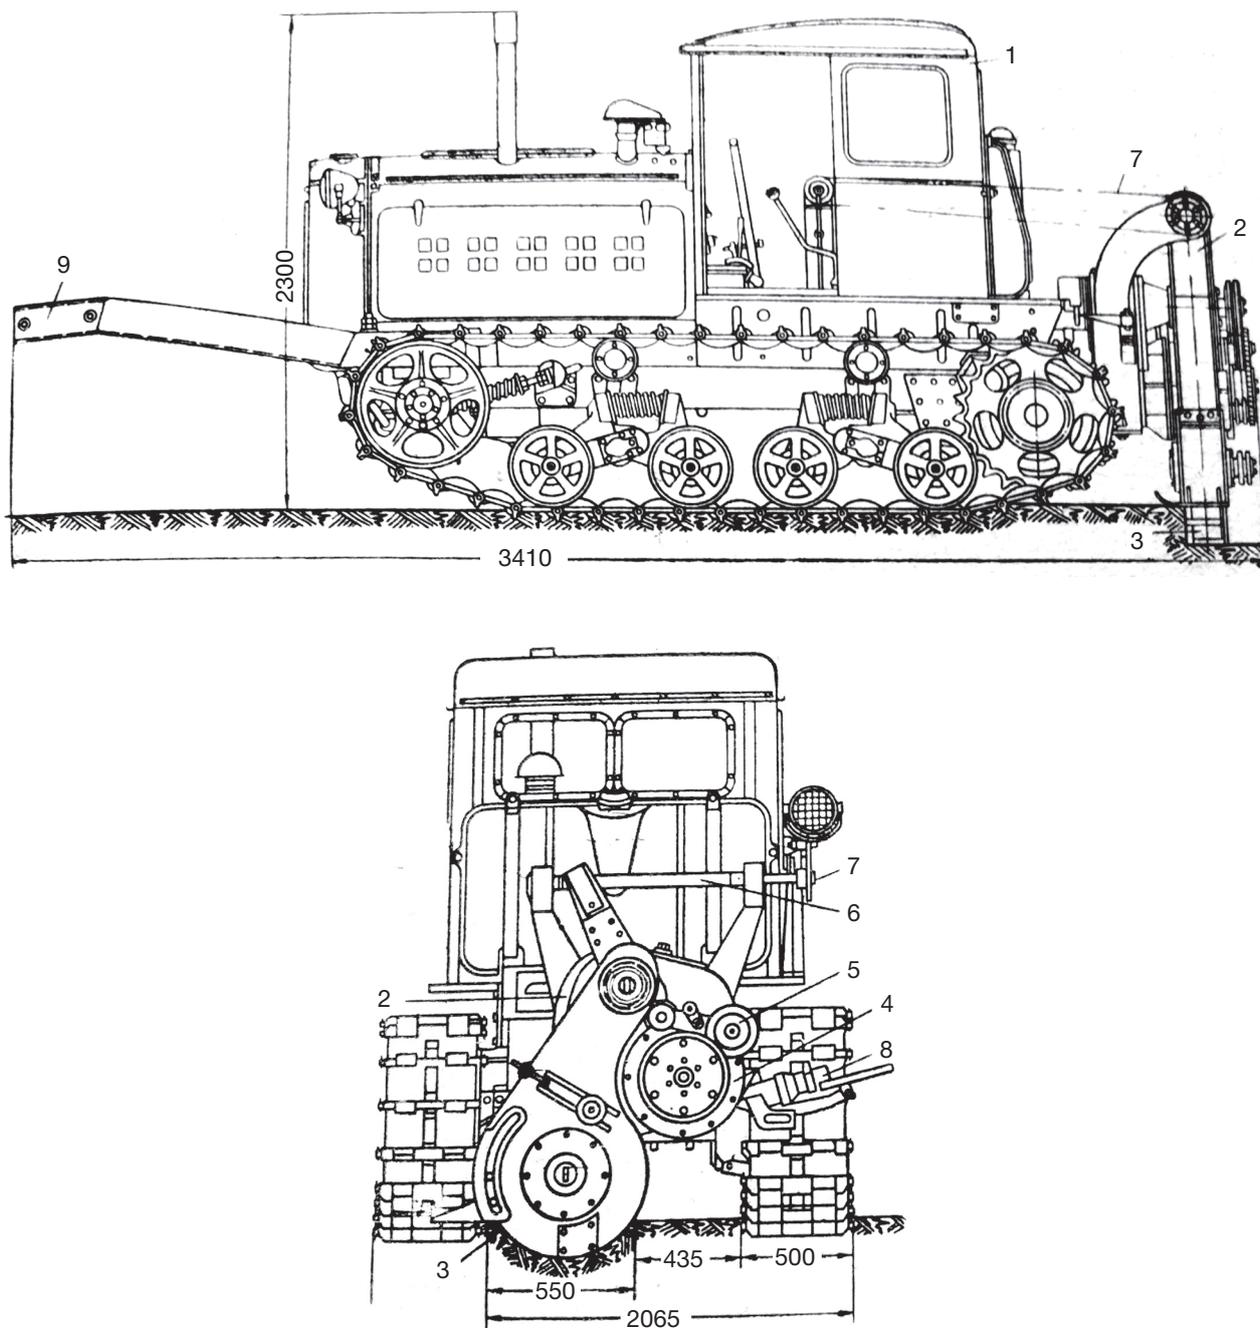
Общий вид машины КДН-2: 1 – кабина гусеничного трактора; 2 – редуктор цилиндрических зубчатых колес; 3 – фреза; 4 – кожух щелевого пресса; 5 – загрузочный барабан щелевого пресса; 6 – винтовой механизм подъема и опускания фрезы; 7 – цепная передача на винтовой механизм подъема и опускания; 8 – мундштук с укладкой торфа в фигуру сушки – валик; 9 – контргруз
